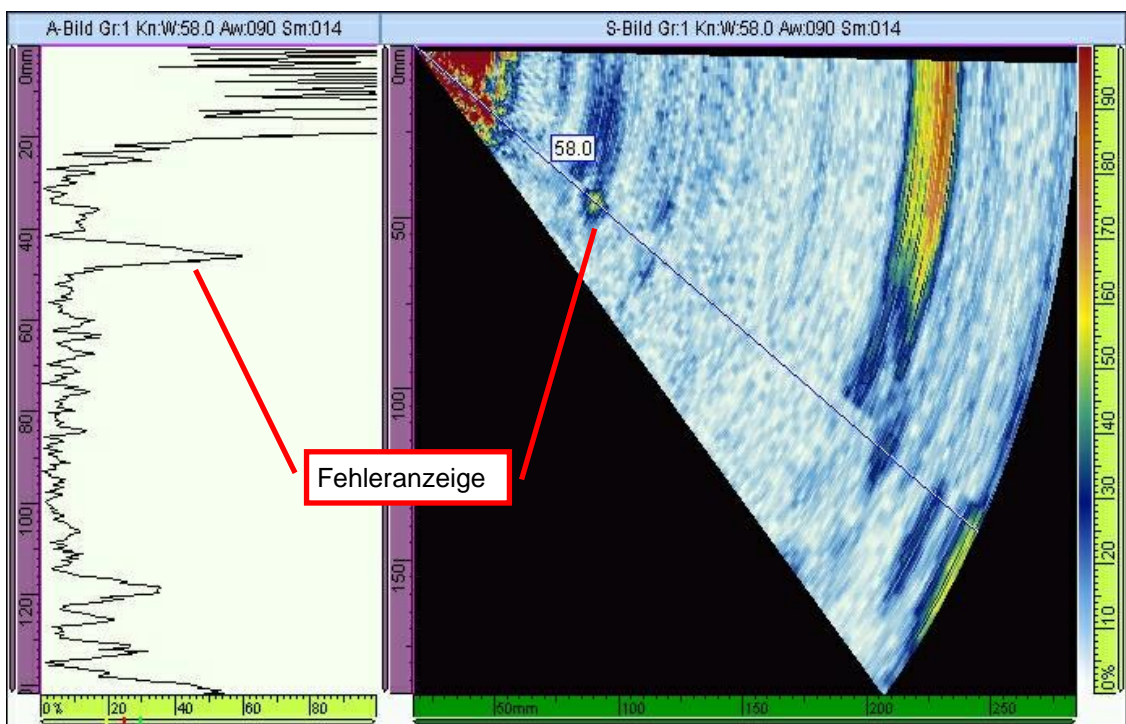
Ultraschall-A-Bild und Sektorscan: 1 mm Testfehler rückseitig hinter der Schweißnaht
